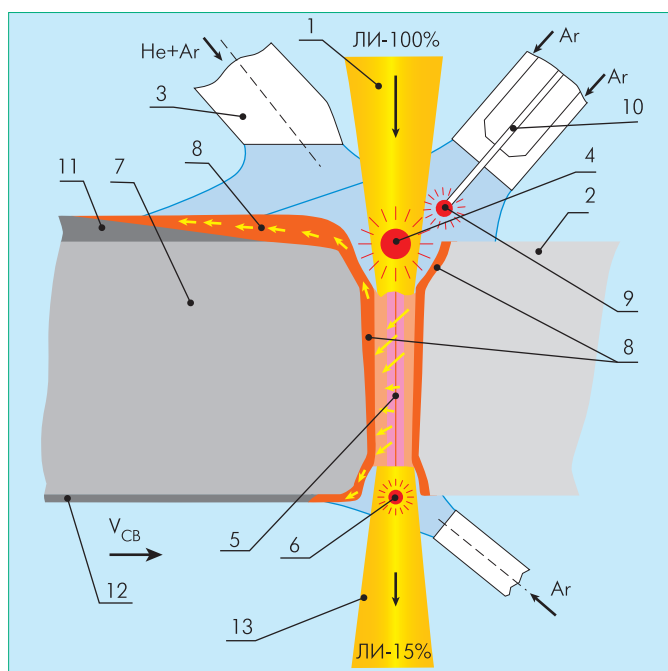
Схема физической модели процесса лазерной и лазерно-дуговой сварки [5, 7]: 1 – лазерный пучок ЛИ, 2 – свариваемое изделие, 3 – защитное сопло для подачи гелия и гелиево-аргоновой смеси, 4 – плазменный факел с лицевой стороны шва (точечный тепловой источник), 5 – "плазменная шуба" внутри парогазового канала (линейно распределенный тепловой источник), 6 – плазменный факел с наружной стороны шва (в случае защиты ее аргоном, точечный тепловой источник), 7 – сварной шов, 8 – сварочная ванна, 9 – сварочная дуга (в случае использования ее для лазерно-дуговой сварки, точечный тепловой источник), 10 – плавящийся (или неплавящийся электрод), 11 – выпуклость сварного шва с лицевой стороны, 12 – выпуклость сварного шва с обратной стороны, 13 – выходящее лазерное излучение
